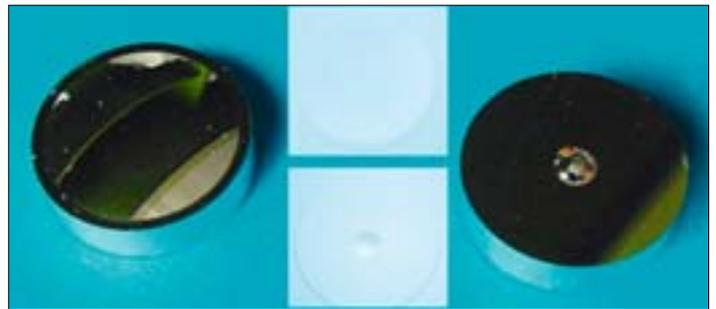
Hohlspiegel in LTCC: Prägewerkzeuge mit optisch glatten Oberflächen und gesinterte Abformungen.
